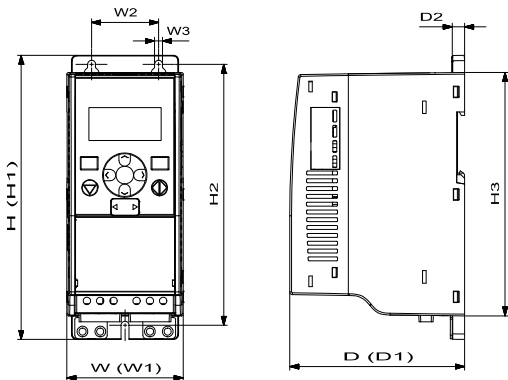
Dimensões do Praxi 20, MI1 - MI3
